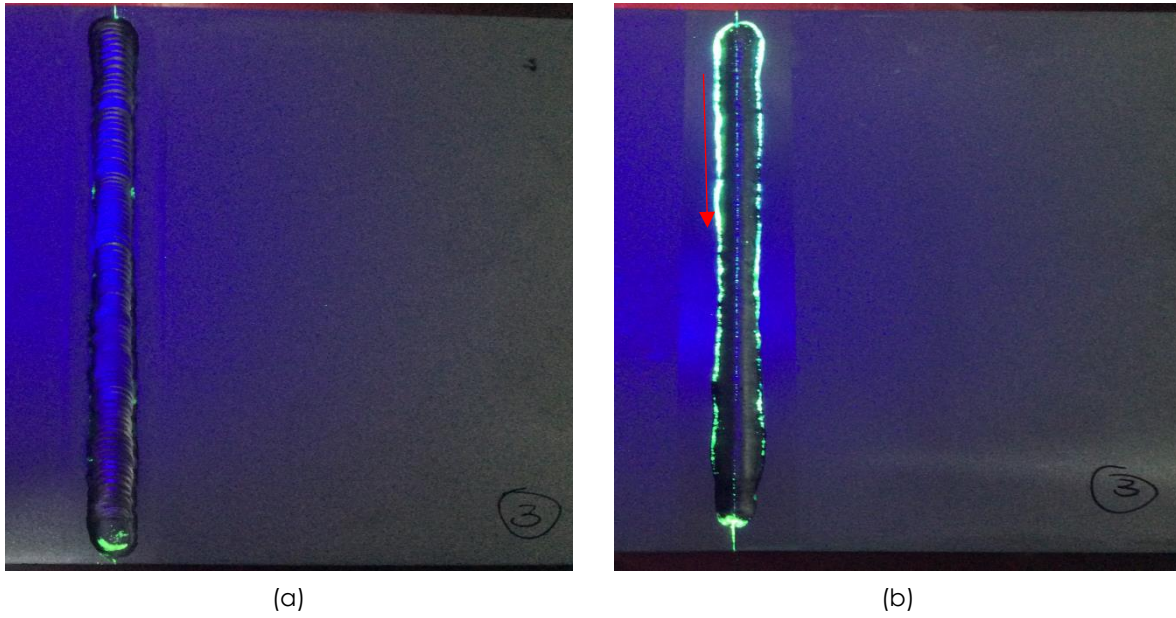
Cordón Soldadura Superior Probeta 3. (b) Cordón de Soldadura Inferior Probeta 3.
